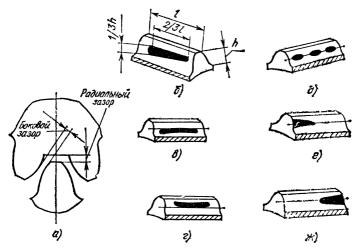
Схемы расположения пятен контакта зубьев при проверке зубчатого цилиндрического зацепления на краску
